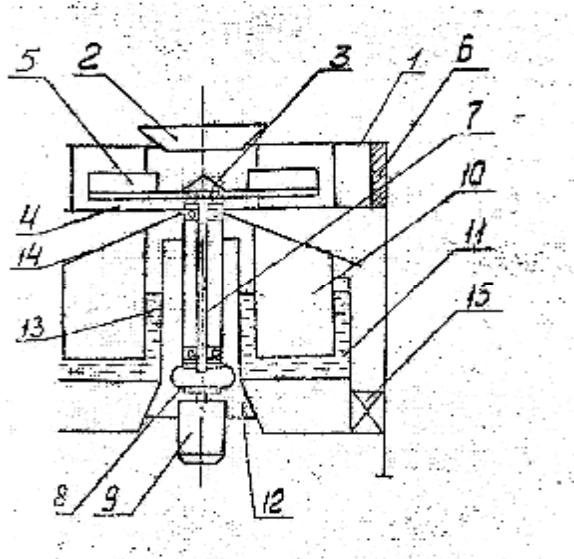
Схема центробежной дробилки ЦД-10 с гидравлической подвеской ротора:
